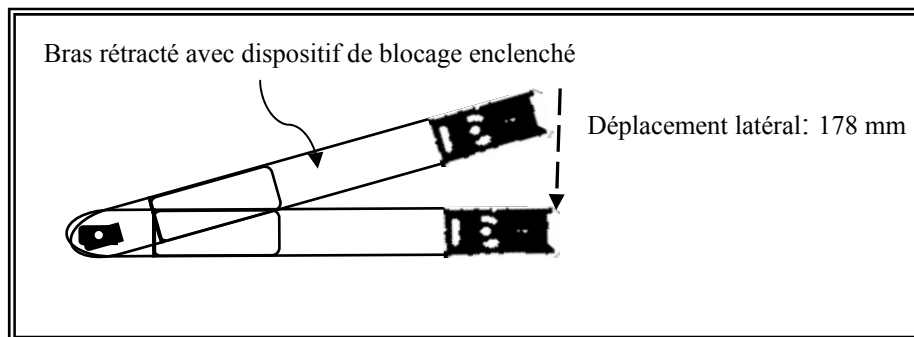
Jeu libre des bras pivotants (vue en plan)
